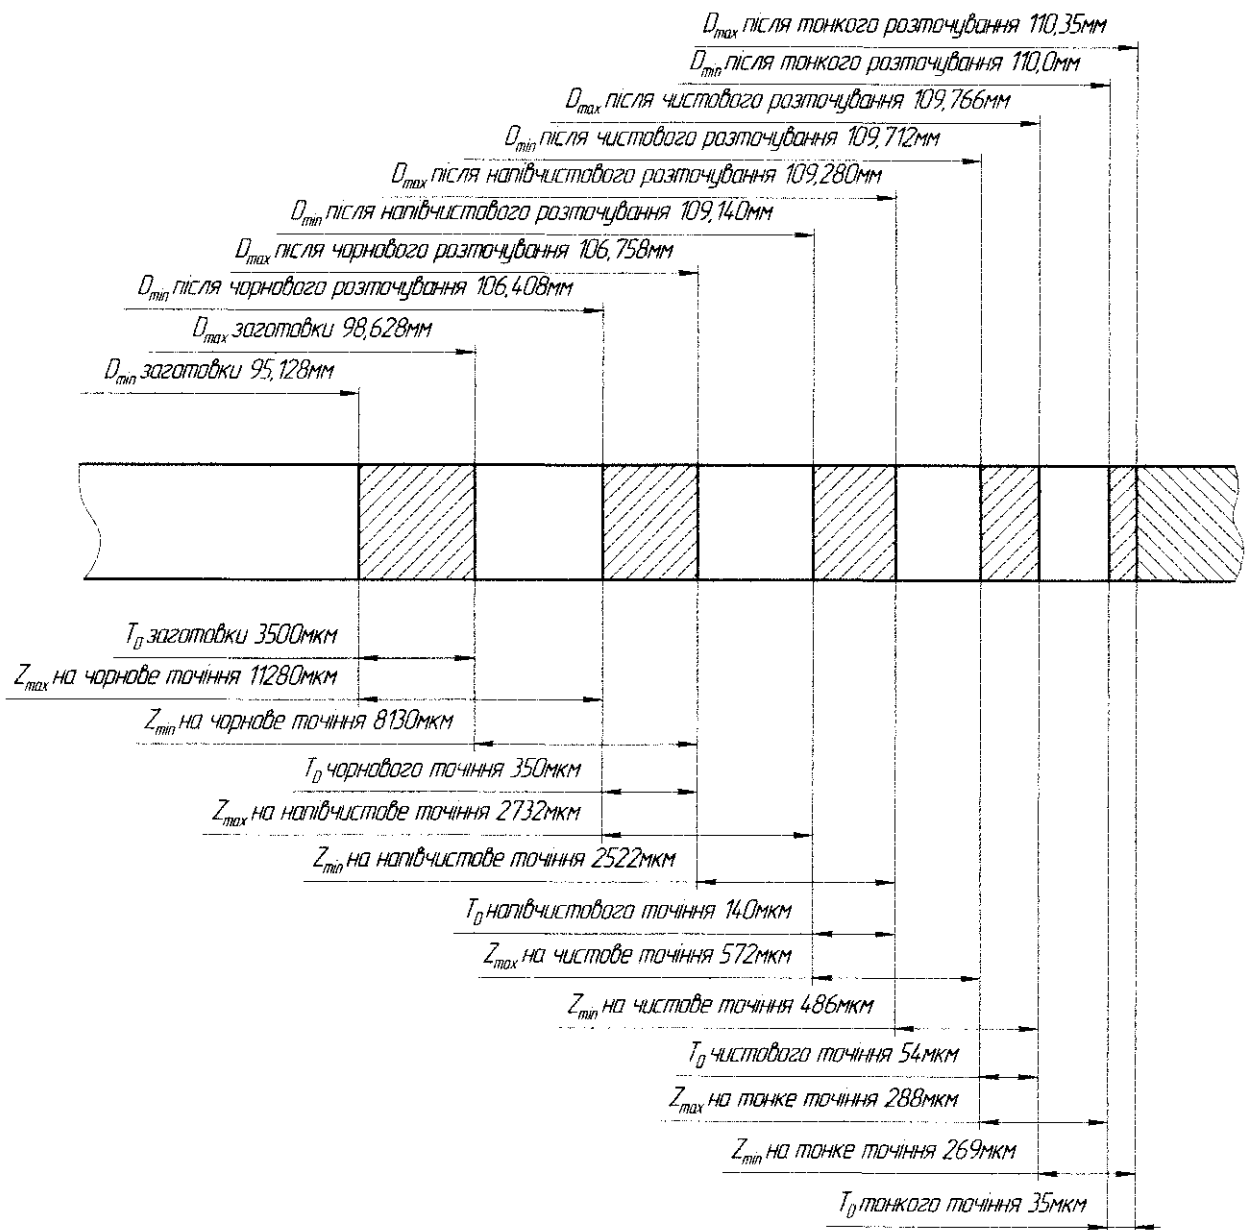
Схема графічного розміщення припусків і допусків на обробку поверхні $\varnothing 110H7$
